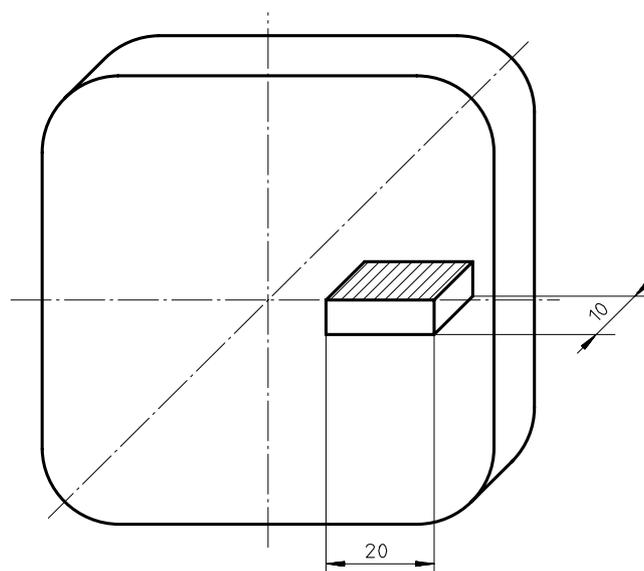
Prélèvement d'échantillon sur barre ou billette de diamètre ou de côté > 40 mm
